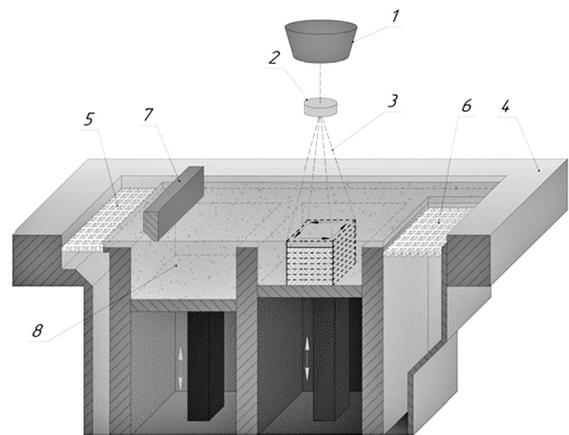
Процесс лазерного плавления порошкового материала: 1 и 2 – лазерное оборудование; 3 – лазерный луч; 4 – стол; 5 и 6 – отверстия для подачи и удаления порошка; 7 – картридж; 8 – слой порошка
